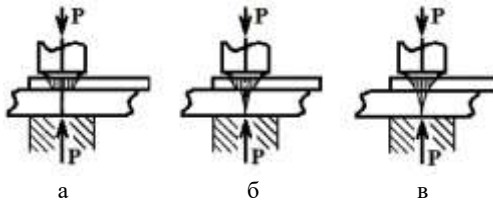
Розповсюдження УЗК при зварюванні: а – початок зварювання; б – процес зварювання; в – кінець зварювання
